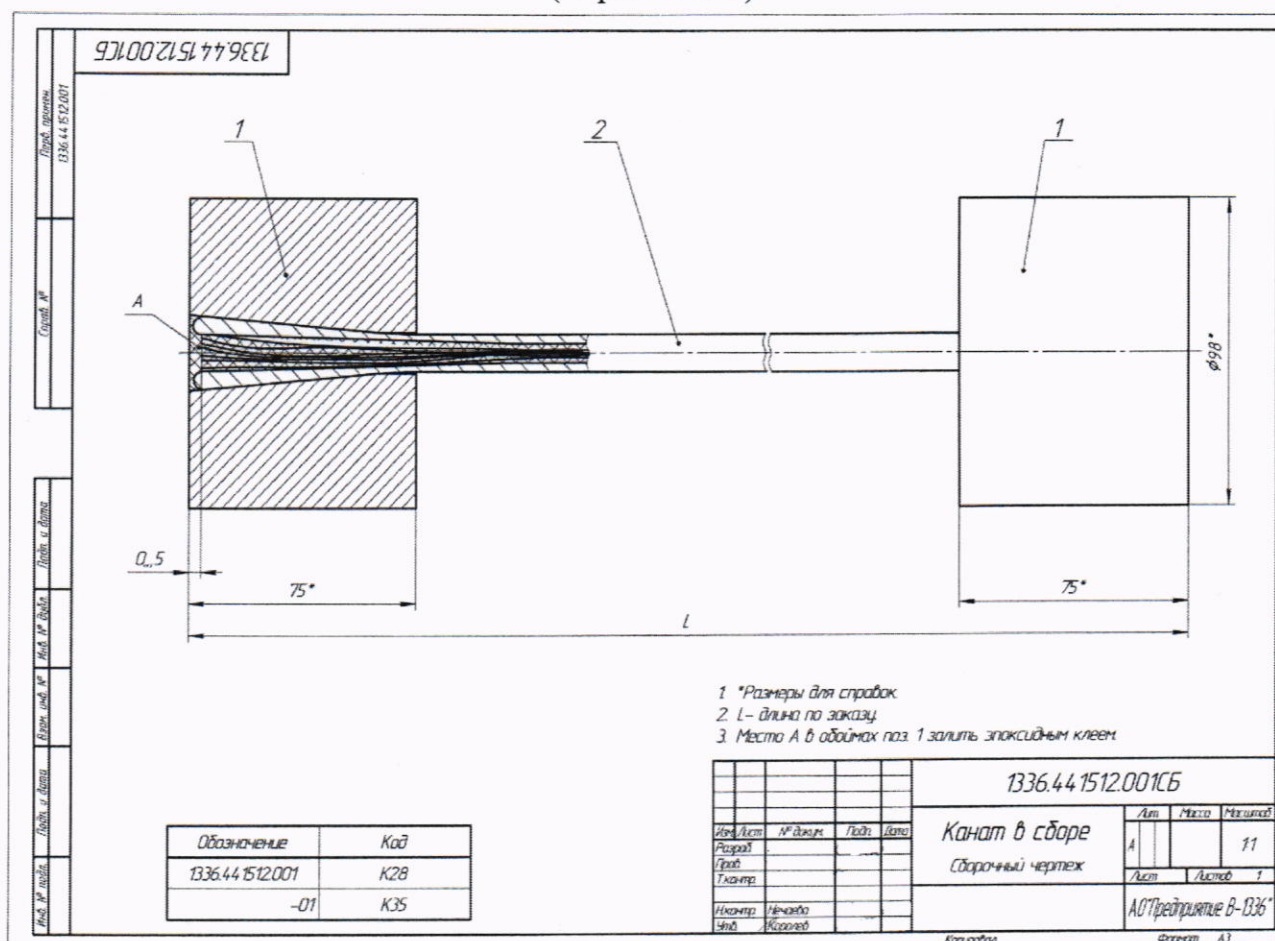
Сборочный чертеж Каната в сборе:
